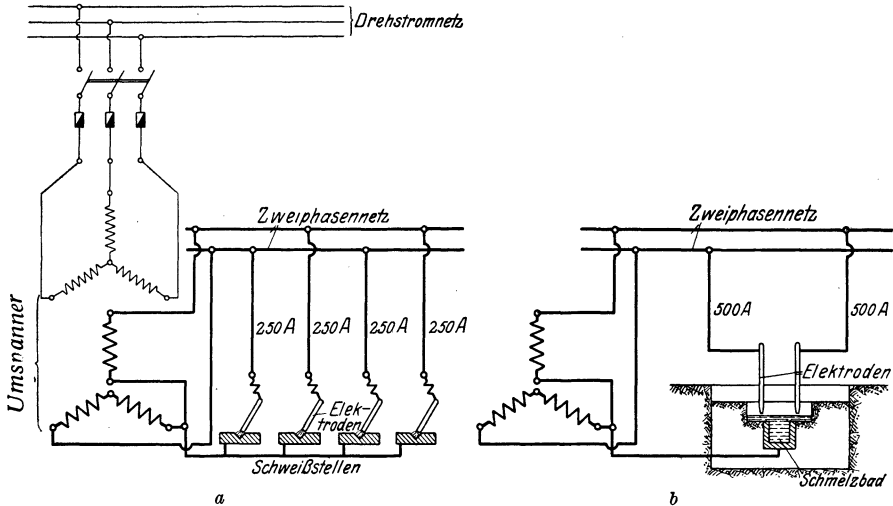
Schweißumspanner mit dreiphasigem Anschluß.
